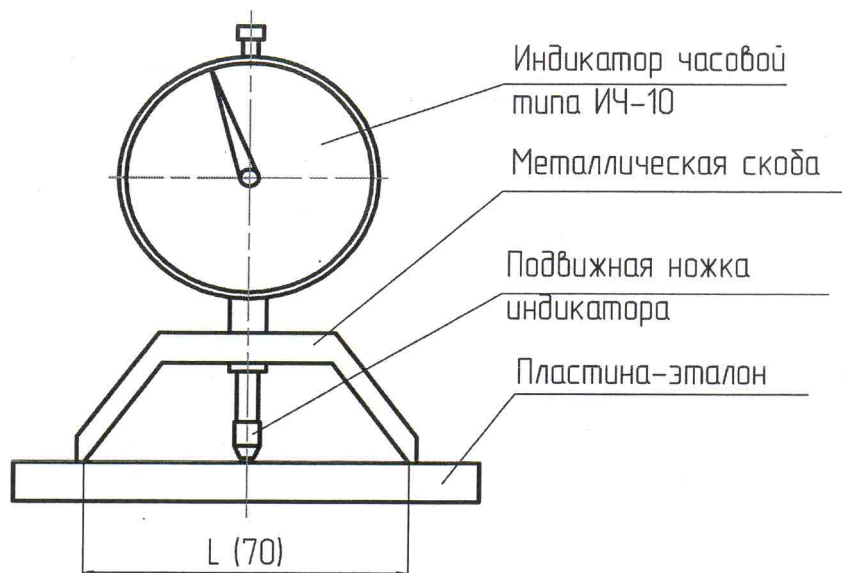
Приспособление для контроля прогиба траверс
